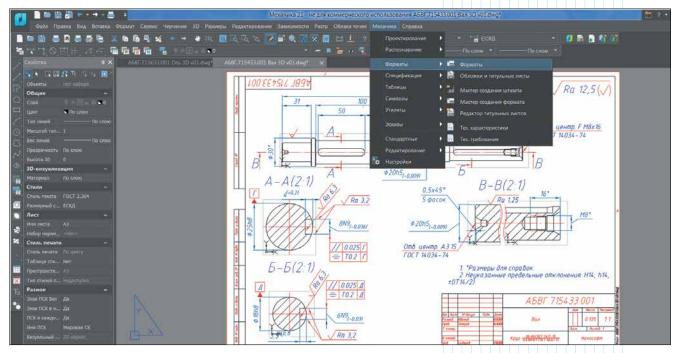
Оформление чертежа вала АБВГ.715433.001
